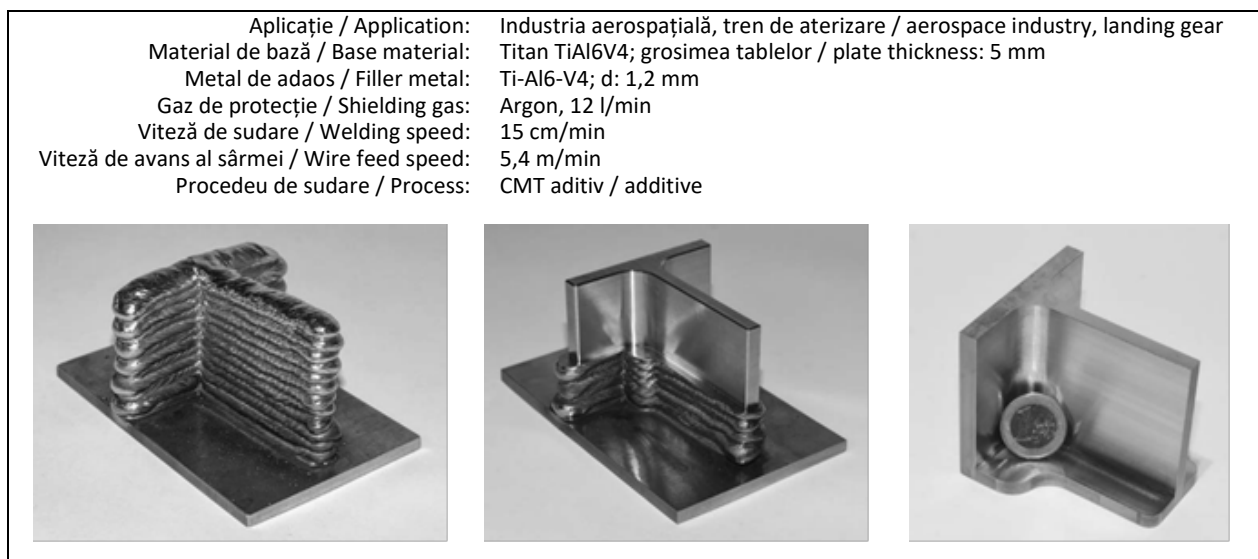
Componentă de construcție realizată din TiAl6V4 (dimensiuni: 70x70x70 mm)
